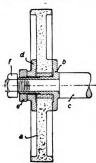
der Schleifscheibe. a Schleifscheibe. b Hülse mit Flansch. c Schleifmit Flansch. c Schleif-spindel. d Loser Flansch. c Mutter für den Flansch. f Spindelmutter.
